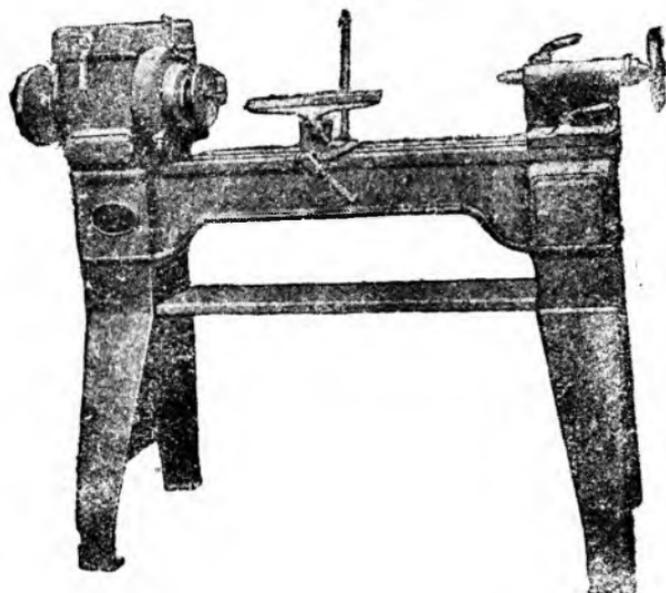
Токарный станок с электромотором на валу шпинделя неподвижной бабки
